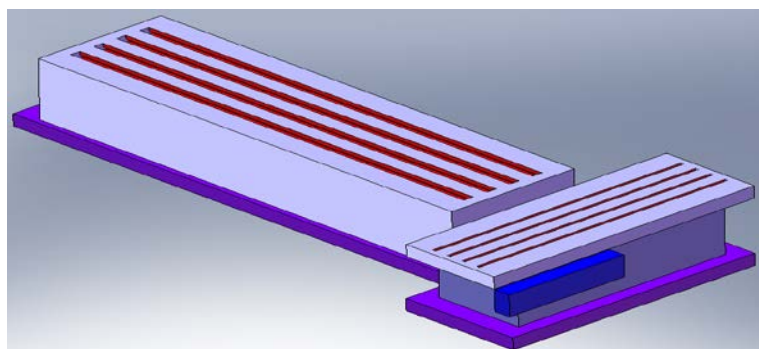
Станина верстата IP500 ПМФ4-09
